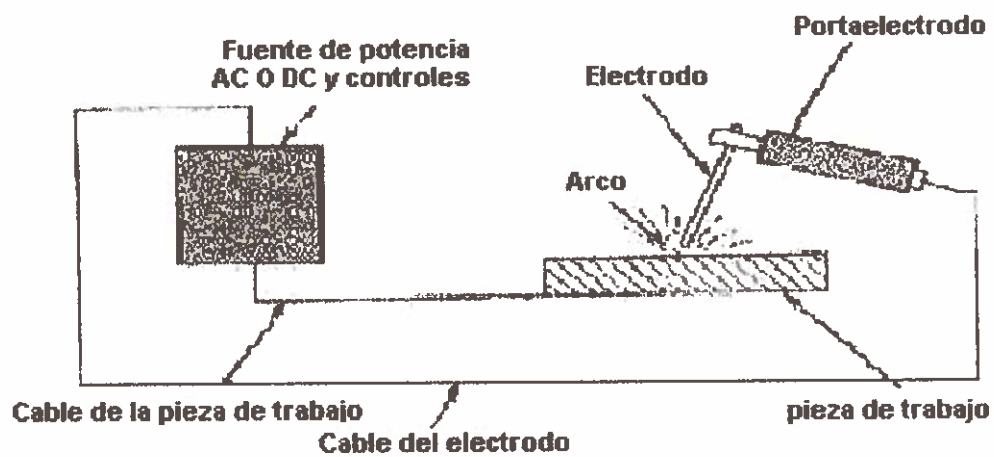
Circuito de soldadura para el proceso SMAW (Ref. 1)
